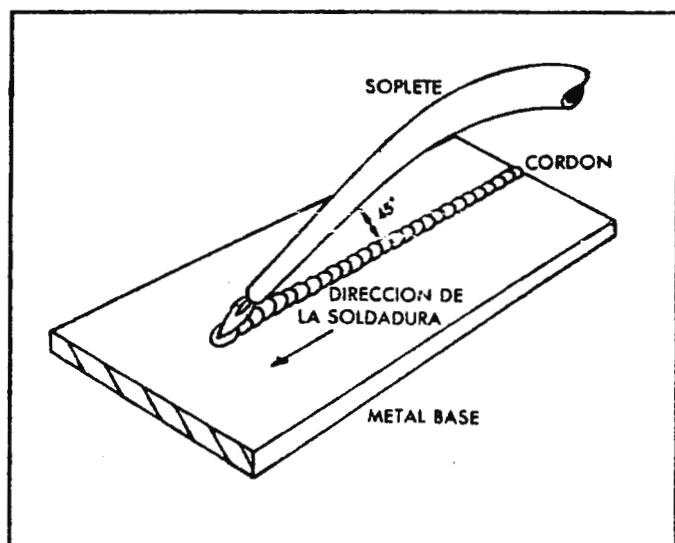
Procedimiento para correr un cordón sin varilla de soldadura
